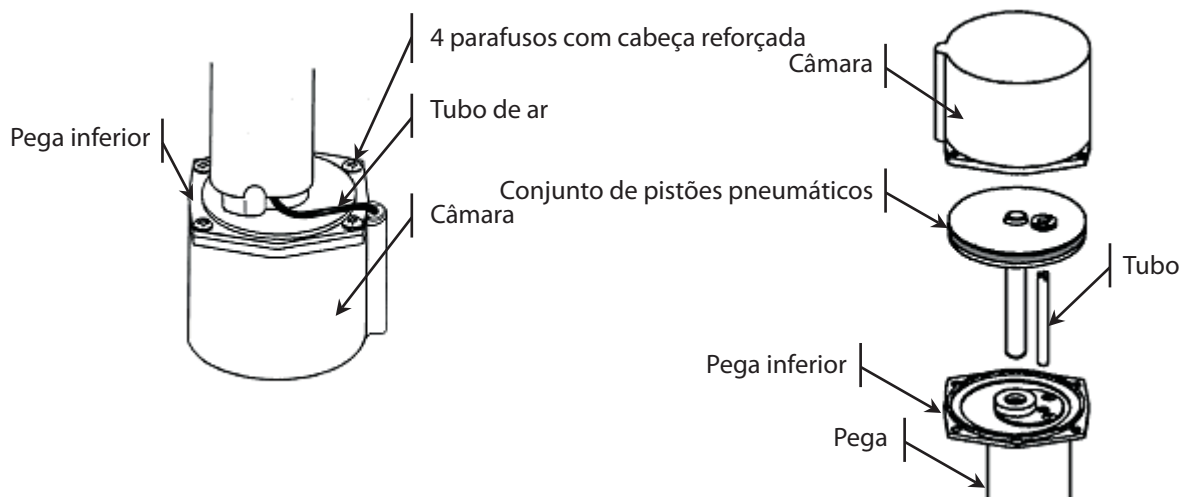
Retirar a câmara e o conjunto de pistões pneumáticos
